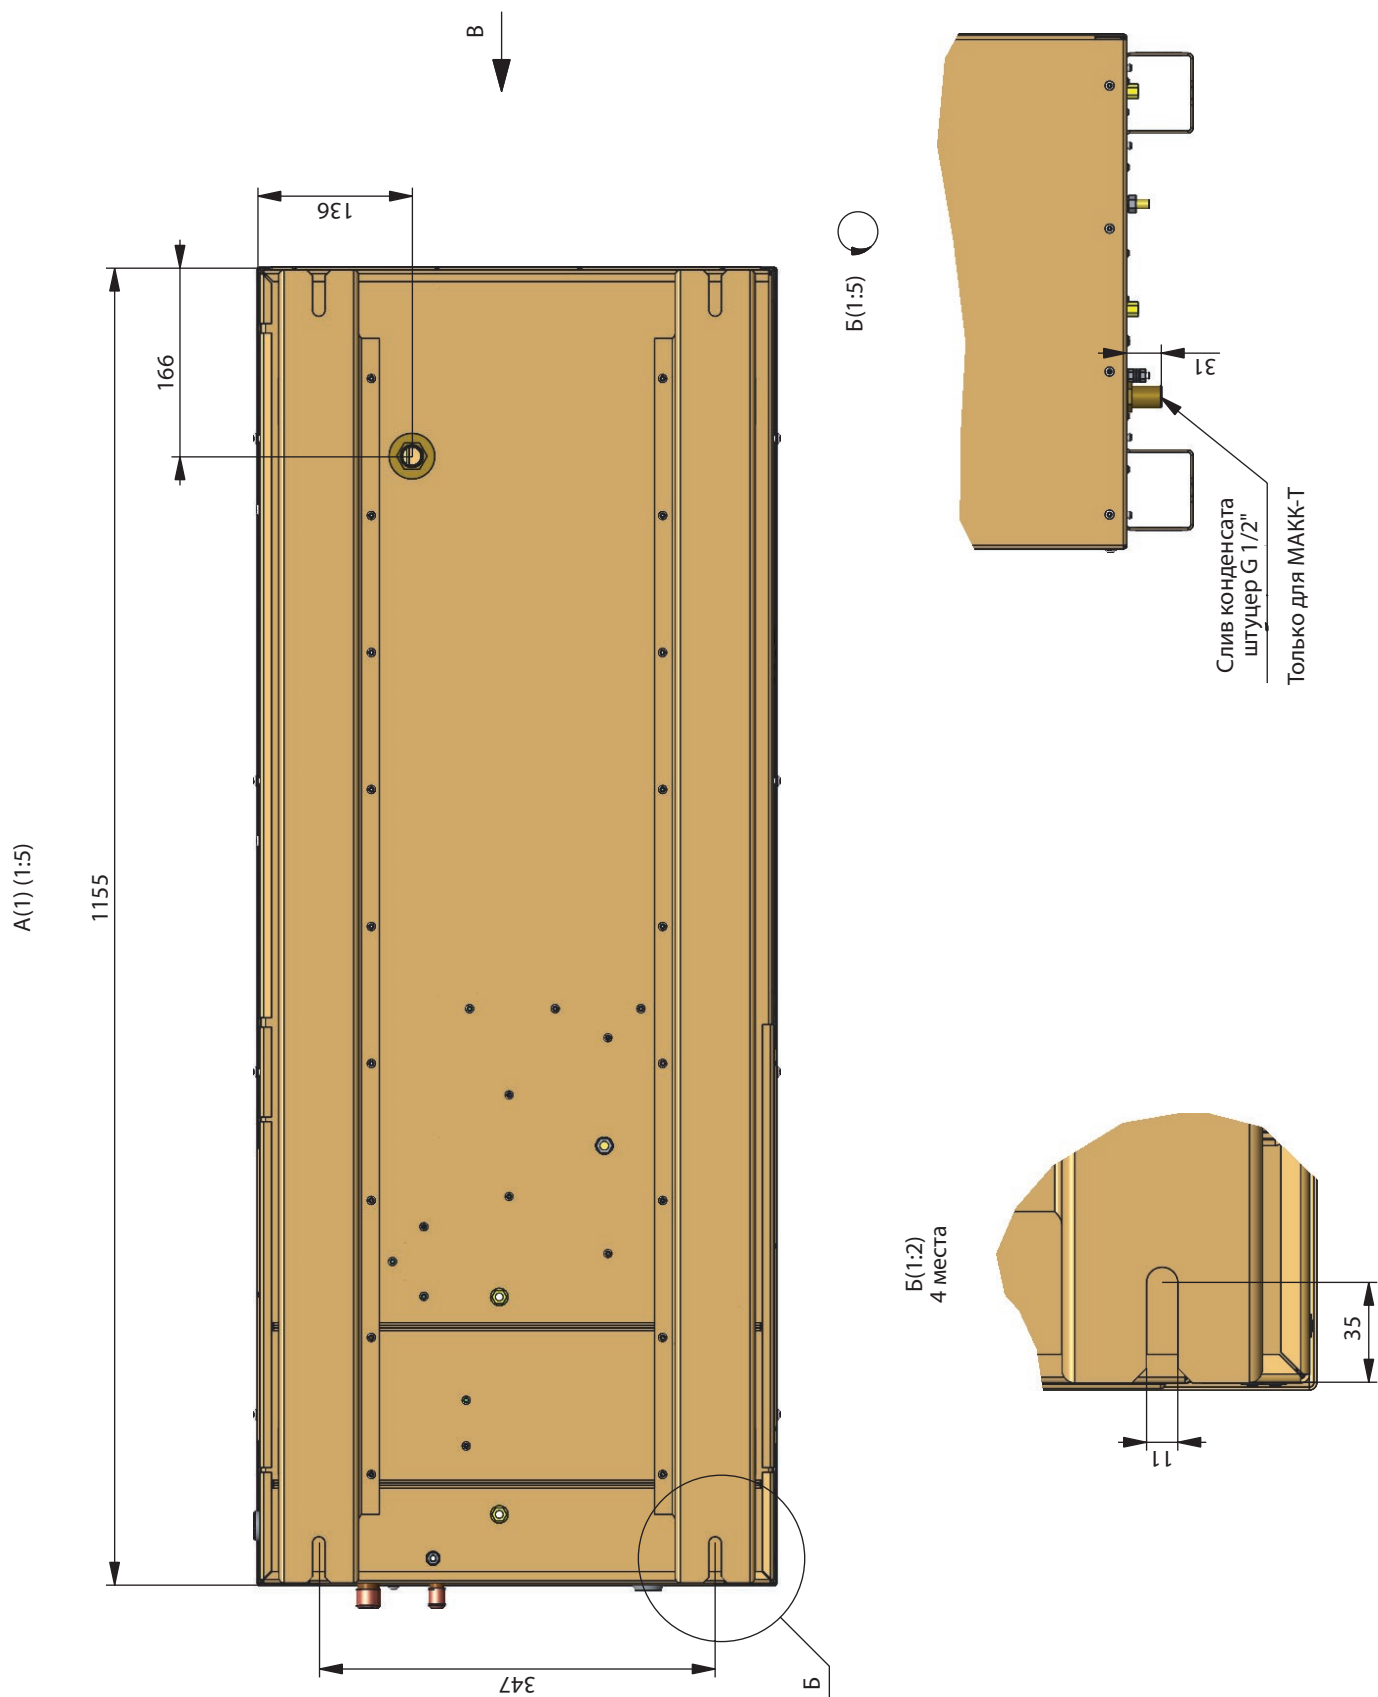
Агрегат компрессорный типа МАКК 110-101, -121, -151
